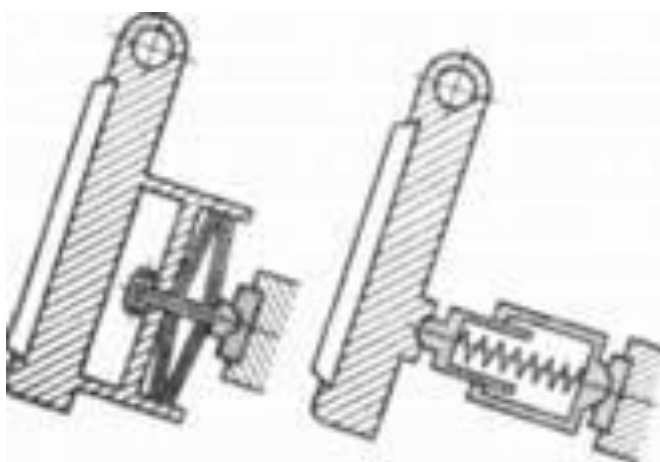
Схема пружинного предохранительного устройства щековой дробилки
